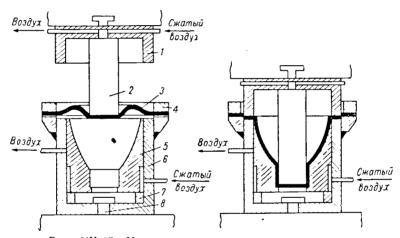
Универсальная пневматическая камера: 1—верхияя камера; 2—пуансон; 3—заготовка; 4—кольцо; 5—матрица; 6—нижняя камера; 7—опорное кольцо; 8—заглушка отверстия для штока.
